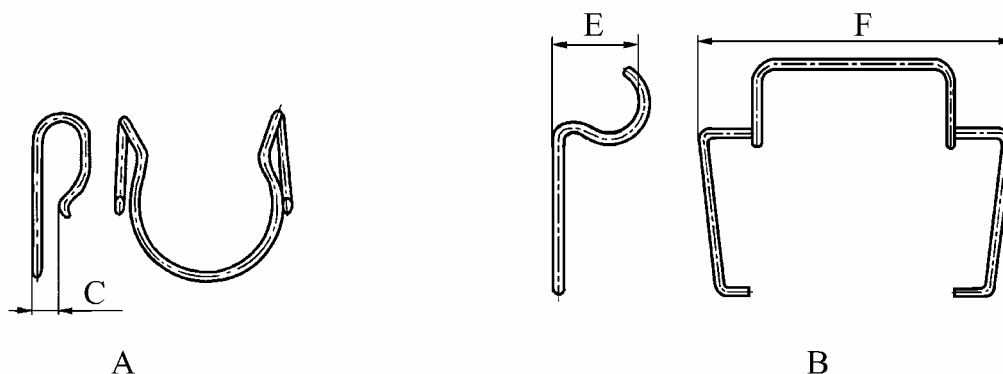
Пружина соединительная вилки и муфты выключения сцепления:
